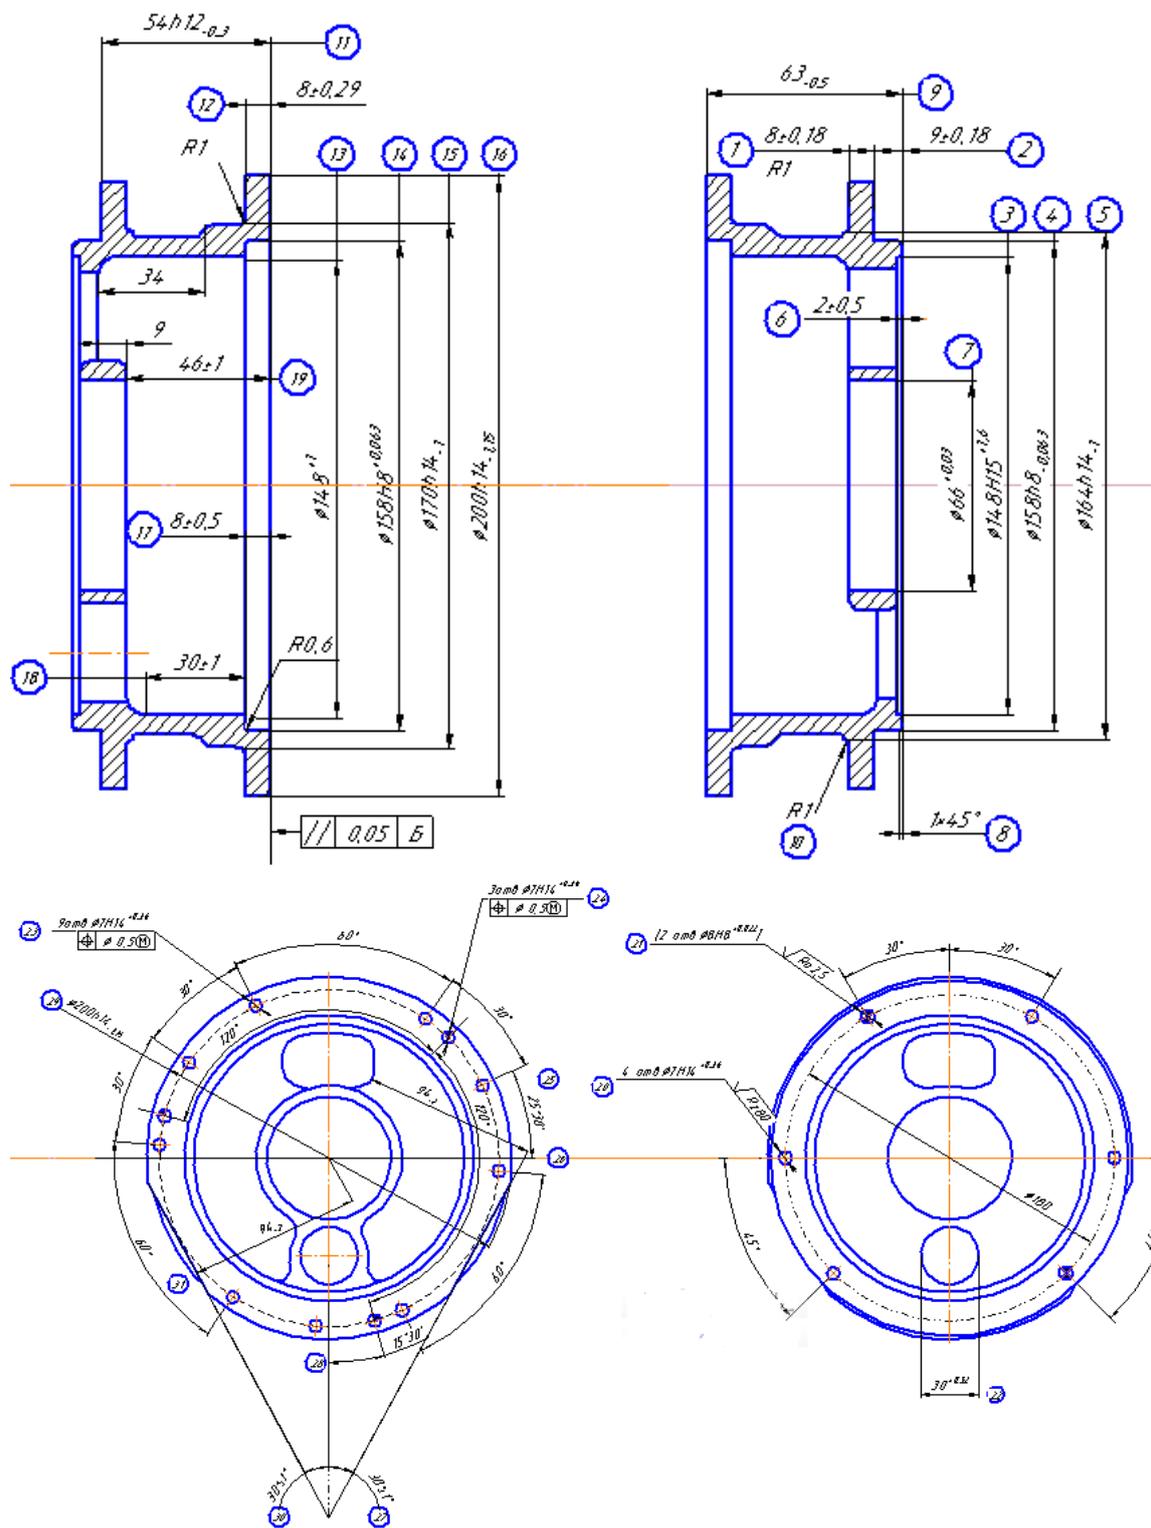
Поверхности детали «Корпуса планетарного редуктора»
